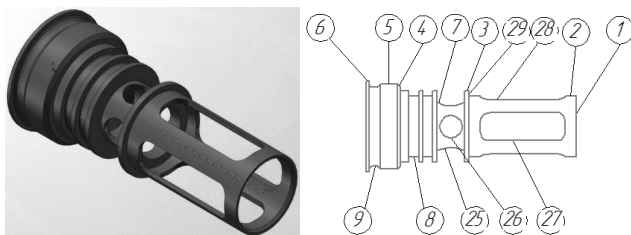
Общий вид детали «Корпус фильтра» и нумерация его поверхностей
